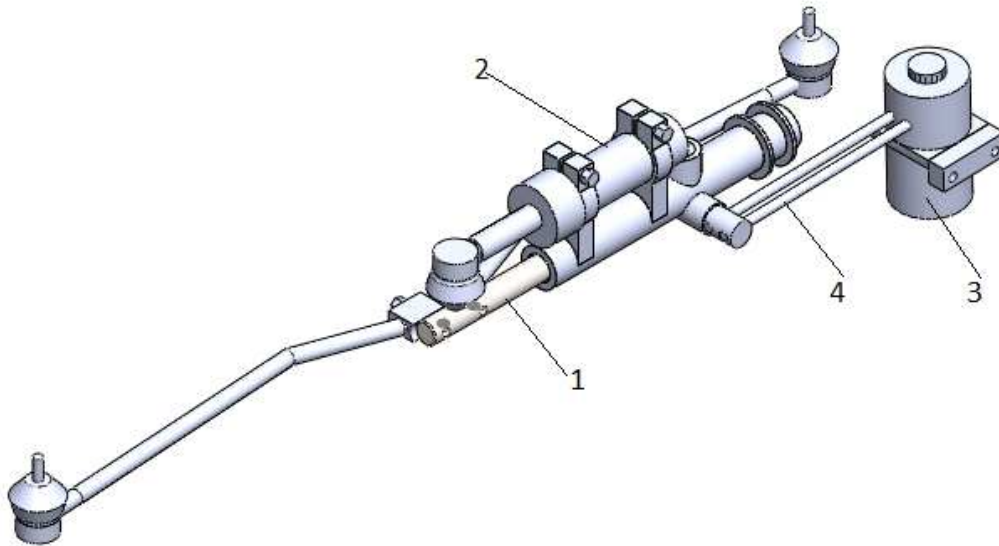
Модель рулевого управления: 1 – рулевой механизм реечного типа; 2 – силовой цилиндр; 3 - шестерёнчатый насос с электродвигателем; 4 – соединительный трубопровод.
